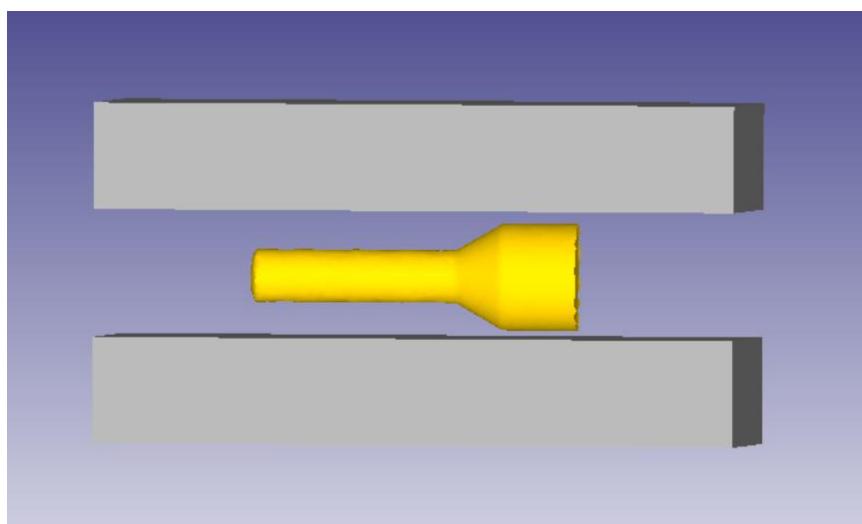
Блок инструментов вместе с заготовкой, который получится после прессования
